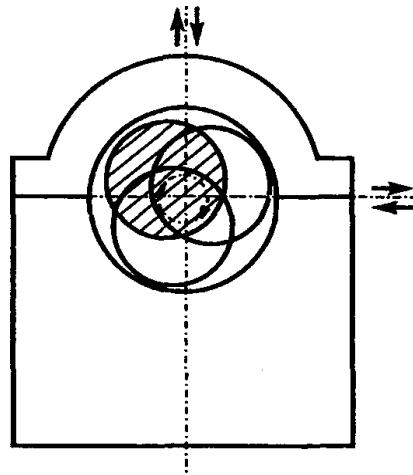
Вибрация цапфы ротора корпуса подшипника
